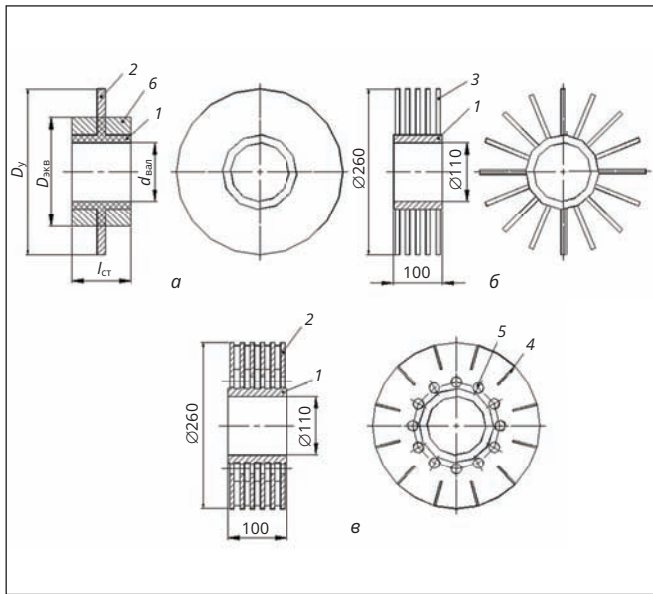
Исследованные устройства воздушного охлаждения вала печного вентилятора Ц9-55 № 10: а — однодисковое ОД 260; б — стержневое СТ 260; в — многодисковое МД 260; 1 — ступица устройства охлаждения; 2 — диск; 3 — стержень; 4 — радиальные лопатки; 5 — впускные отверстия; 6 — условная эквивалентная втулка; $D_{экв}$ — диаметр эквивалентной втулки; D_y — внешний диаметр устройства; $l_{ст}$ — длина ступицы устройства охлаждения; $d_{вал}$ — диаметр вала вентилятора
